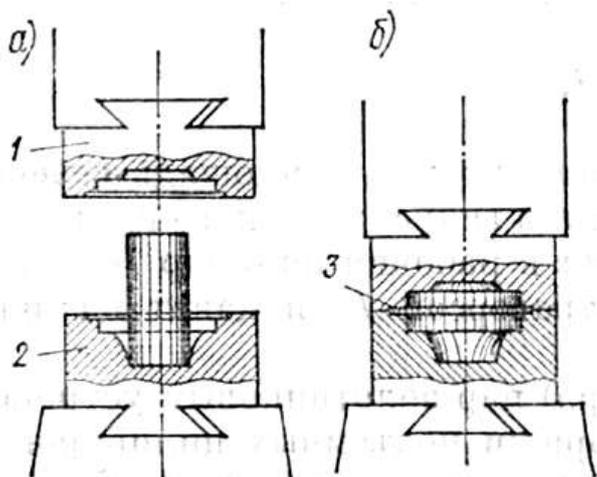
Схема одноручьевого штампа: 1-верхний штамп; 2-нижний штамп
